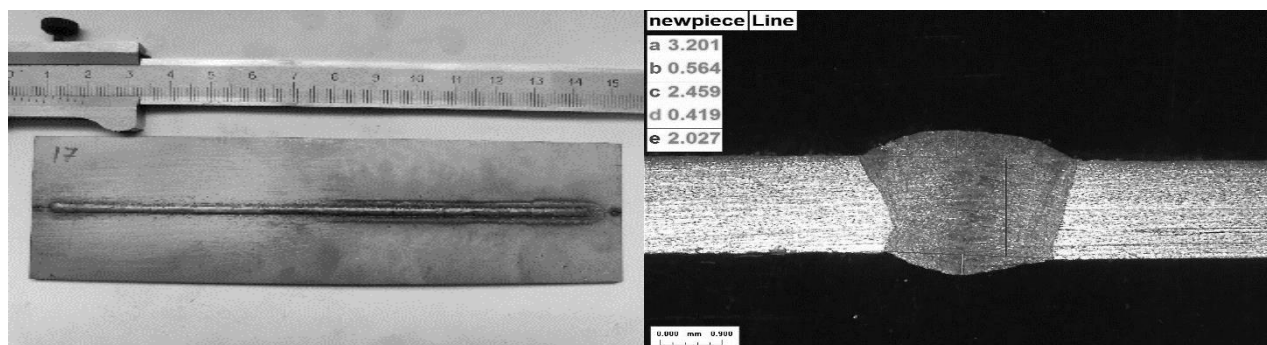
Внешний вид и шлиф стыкового сварного соединения пластин (без зазора) из нержавеющей стали с коаксиальной подачей порошка
